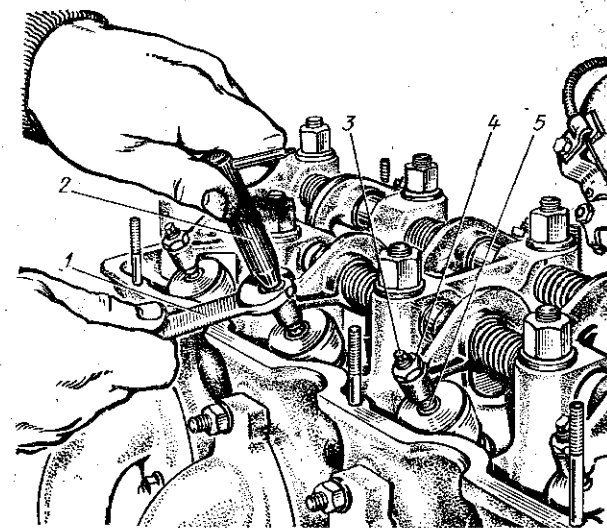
Регулировка зазора между торцами наконечника и стержня клапана:
